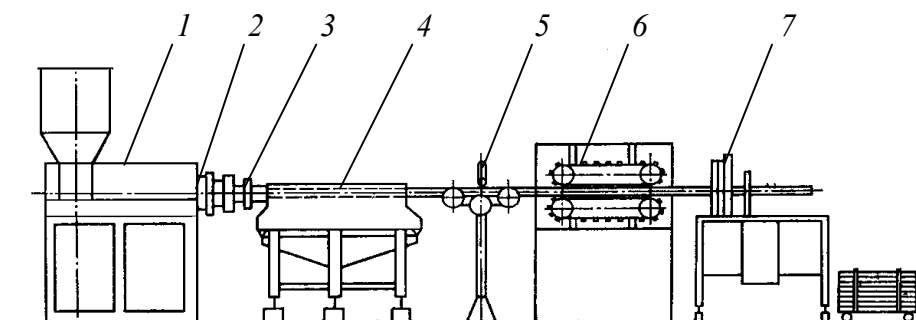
Схема лінії для виробництва труб із ТпМ на базі черв'ячного екструдера: 1 – черв'ячний екструдер; 2 – трубна головка; 3 – калібрувальний пристрій; 4 – охолодний пристрій; 5 – маркувальний пристрій; 6 – тягнучий пристрій; 7 – відрізний пристрій
